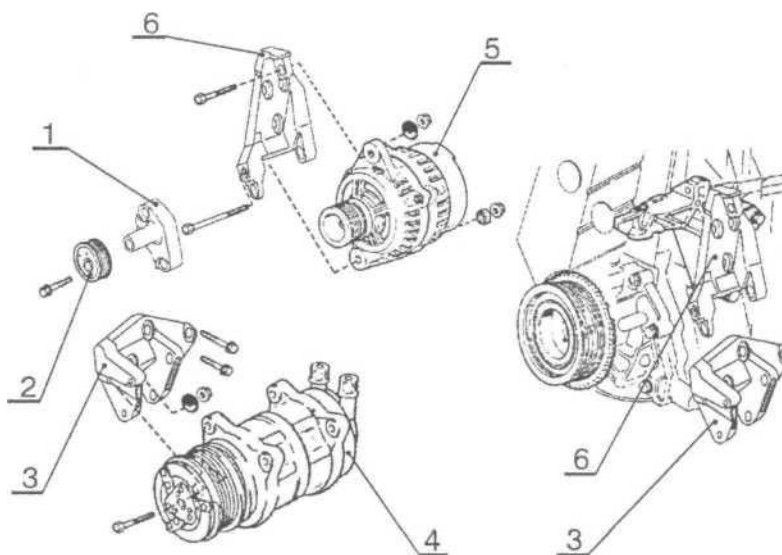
Монтаж элементов климатической установки на двигатель: 1 - кронштейн натяжителя; 2 - ролик натяжной; 3 - кронштейн подушки штанги подвески двигателя; 4 - компрессор; 5 - генератор; 6 - кронштейн генератора.
